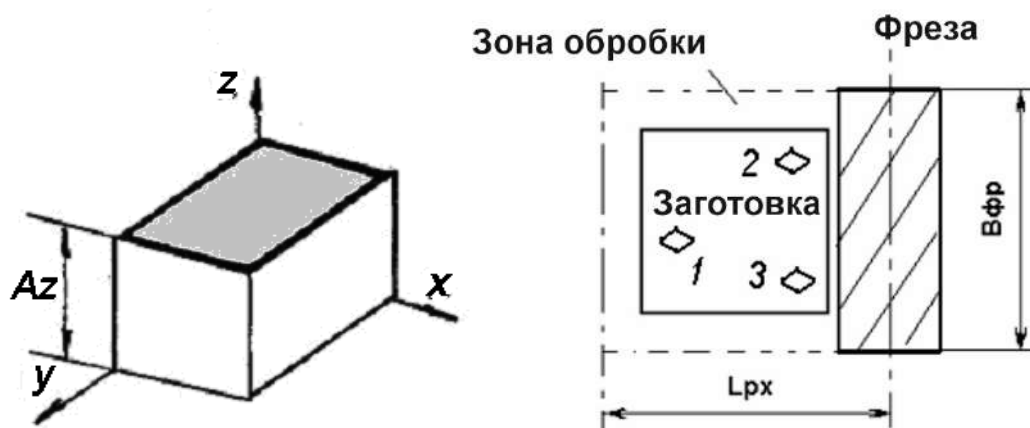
Базування заготовки по площині основи на столі верстата
